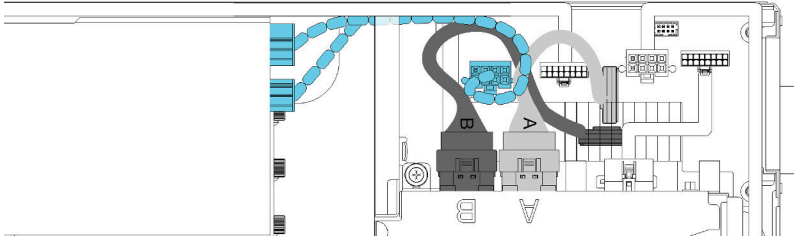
Disposición de PCIe#1-A, PCIe#2-B y del cable de alimentación auxiliar de expansión frontal
